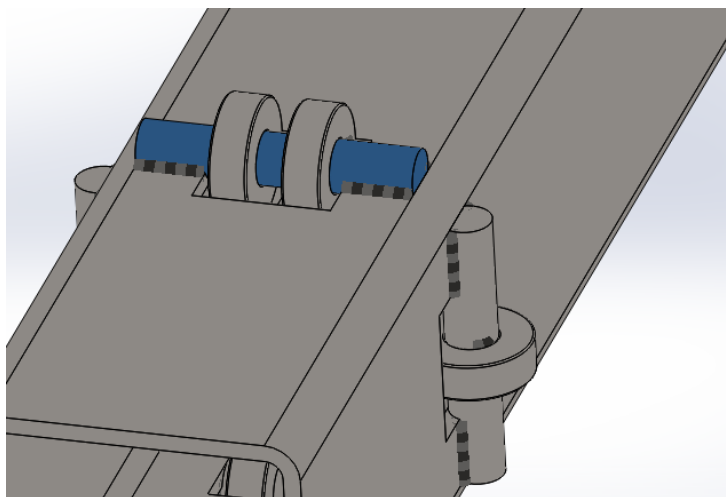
Detalle de conjunto de rodamientos soldados sobre tubo de 100
